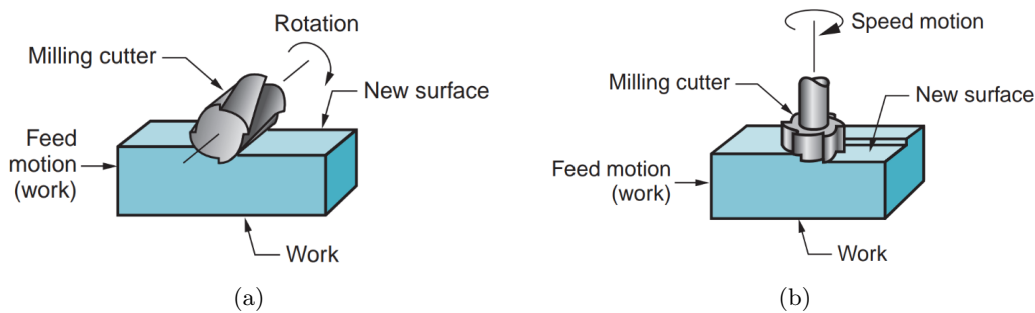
Esquema de maquinagem de objetos pelo processo de fresar: cilíndrica (a) e frontal (b) [53]
